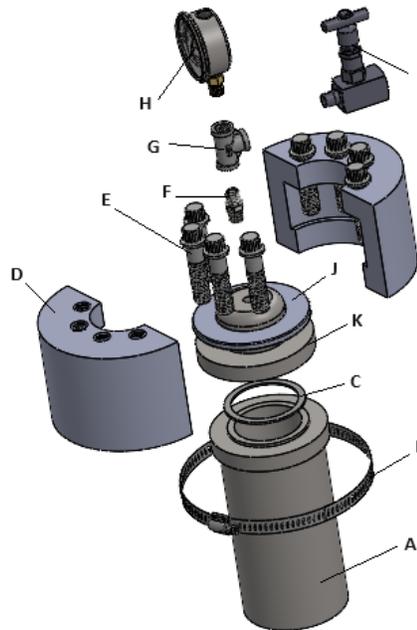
Ensamble explosionado del sistema de extracción por CO₂ supercrítico.
